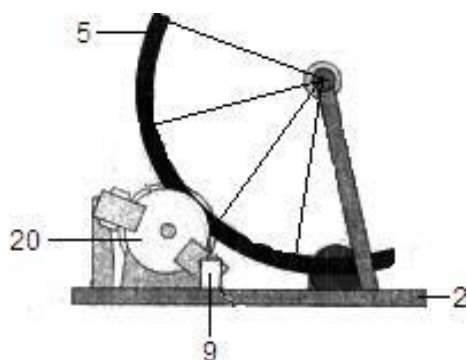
Вид регулирующего устройства со стороны медного диска.
